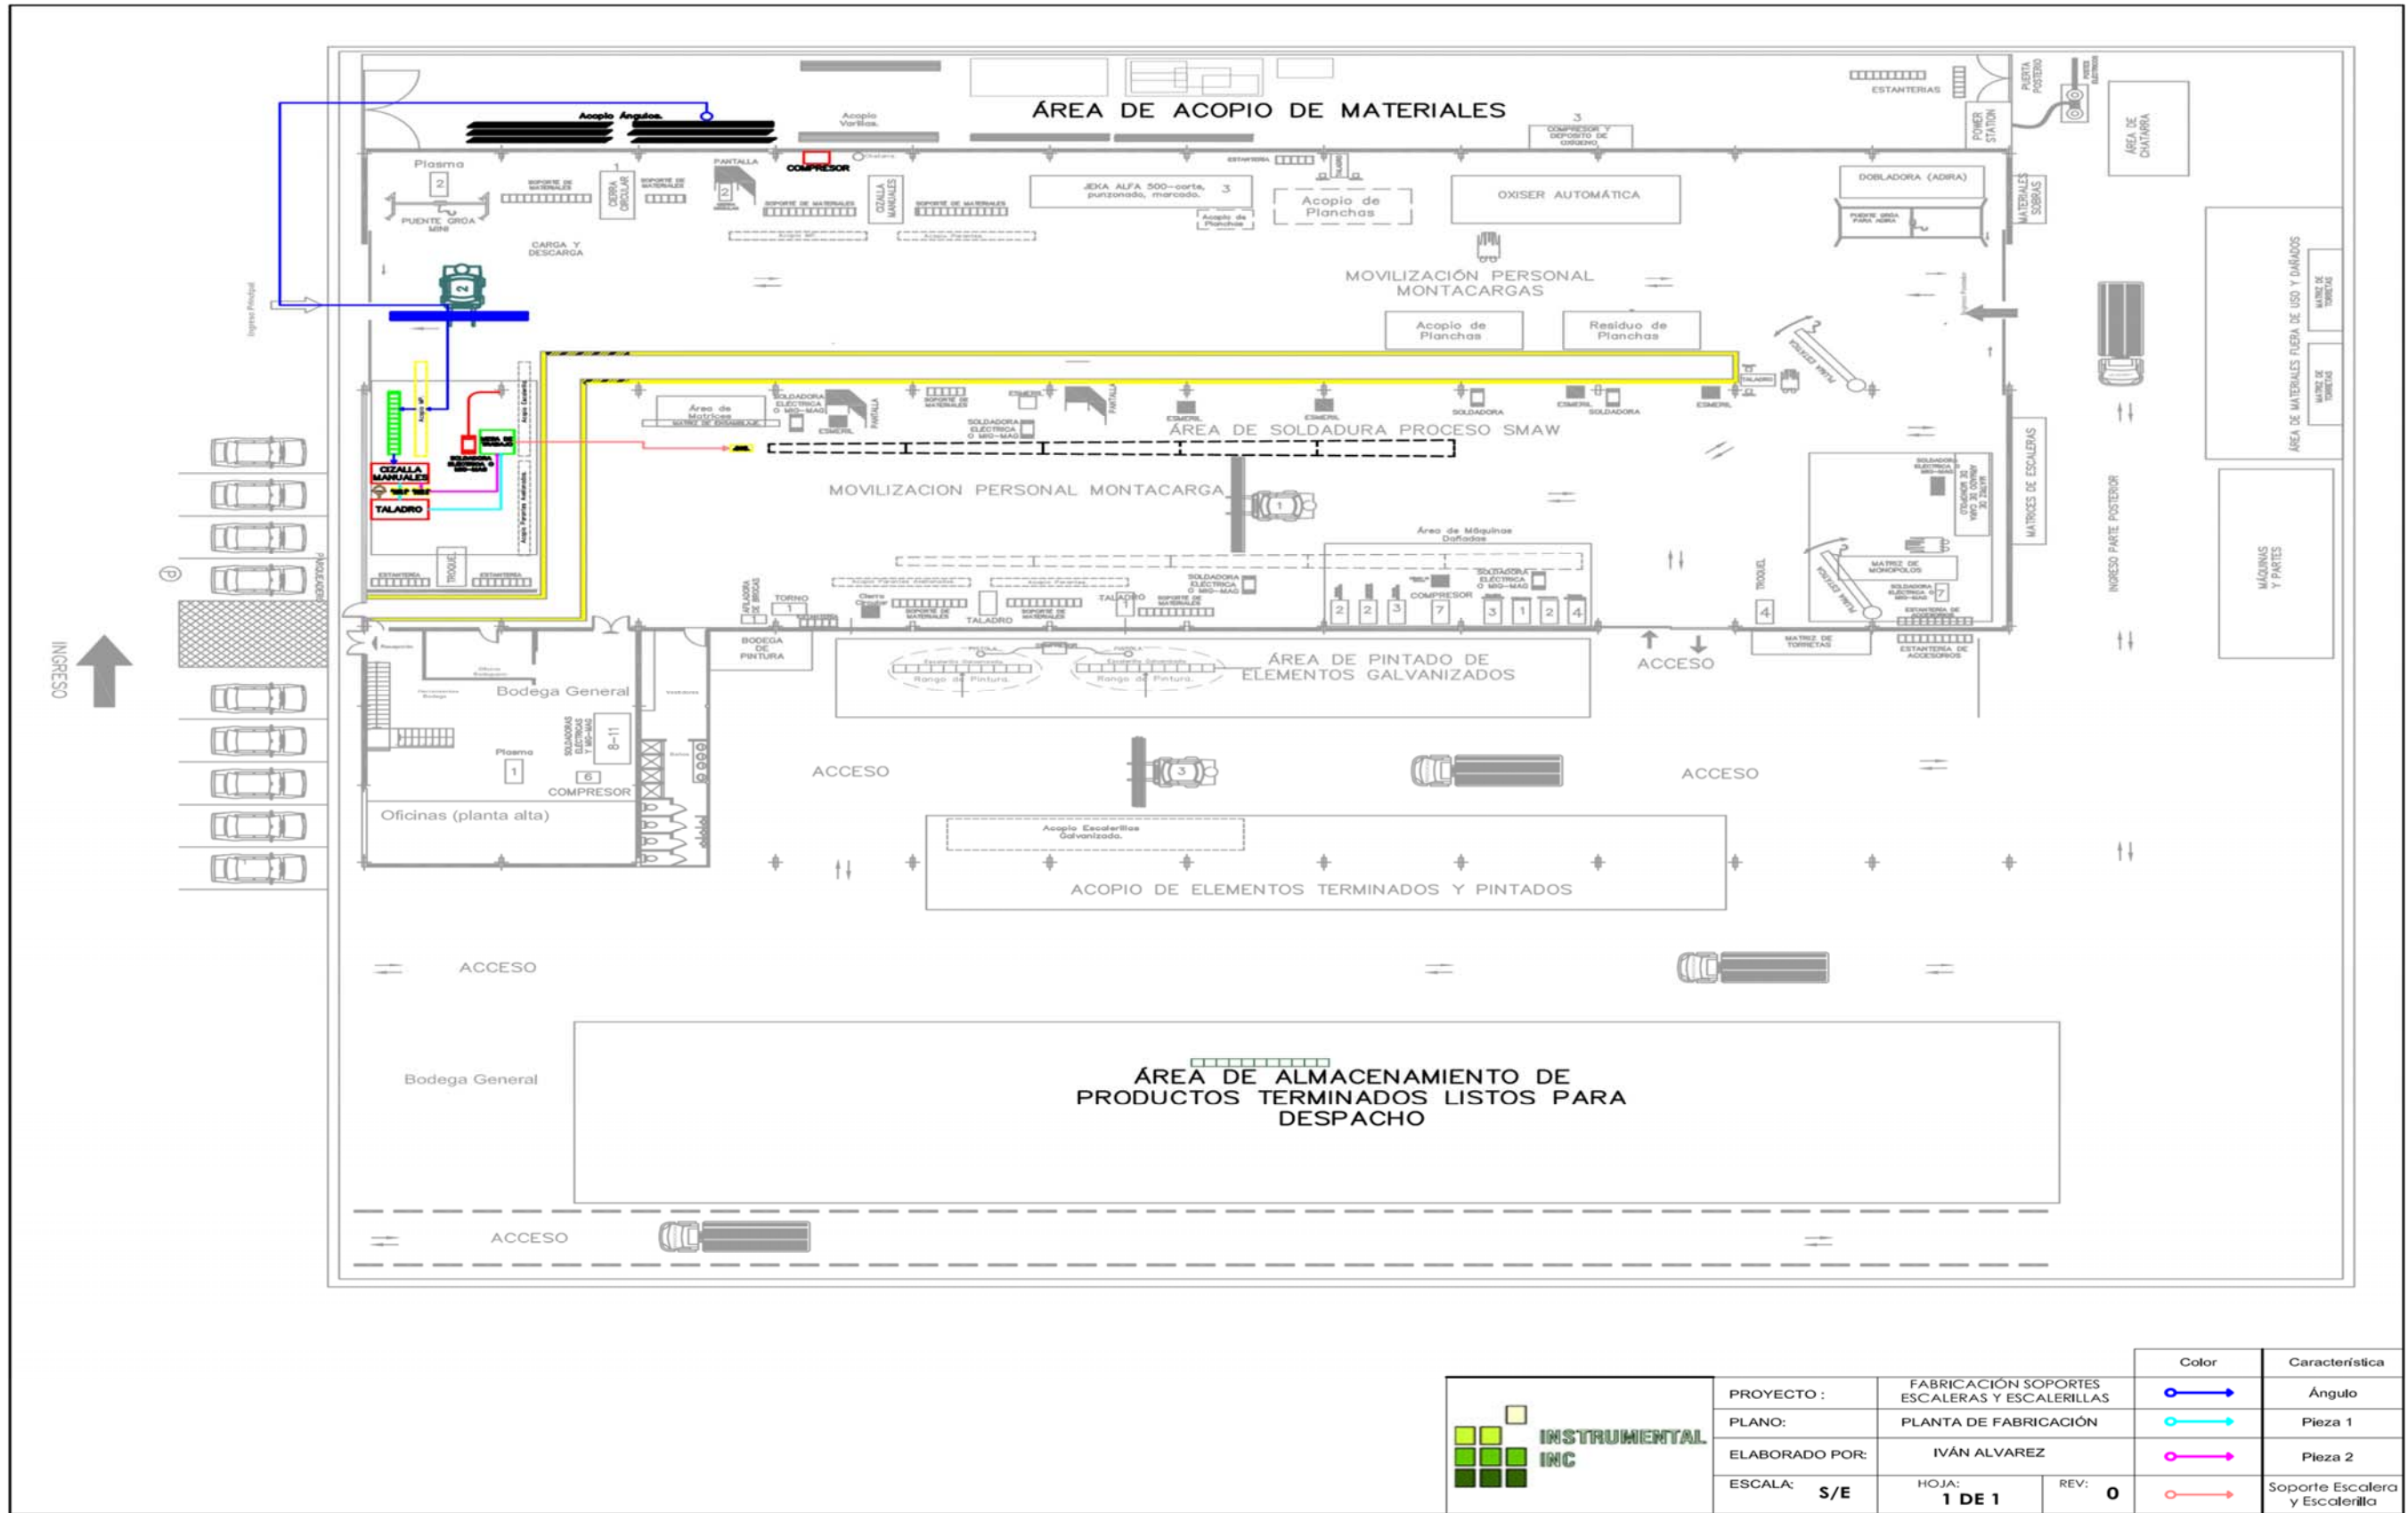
Fabricación Soporte de Escaleras y Escalerillas Después.
